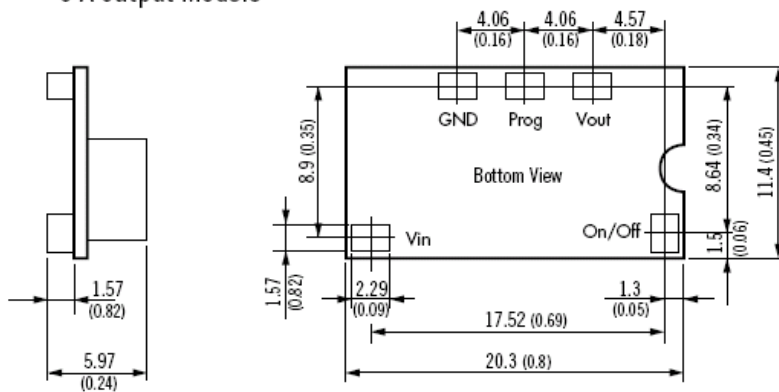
Чертеж корпуса моделей TOS 06-05SM, TOS 06-12SM
